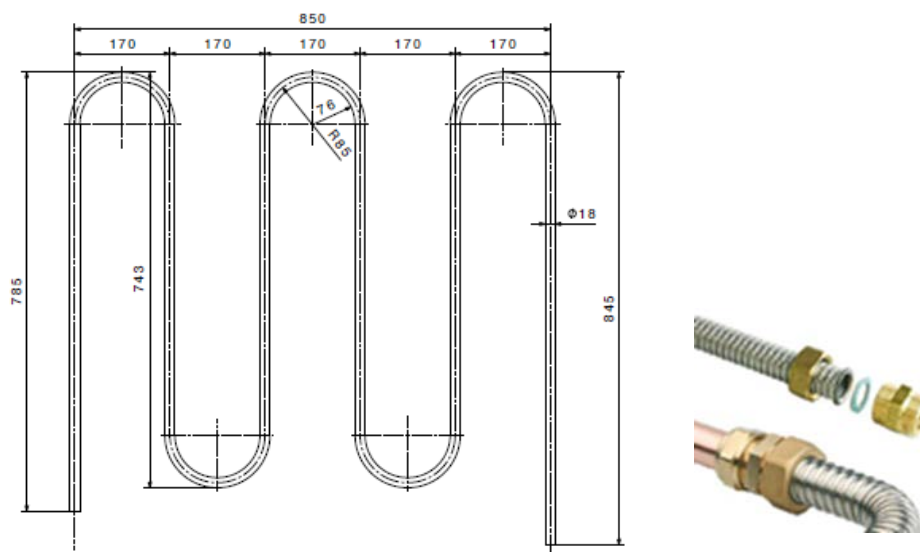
Dimensionierung der in die einzelnen Betonelemente eingegossenen Kupferschlaufen mit Anschlussfittings.
